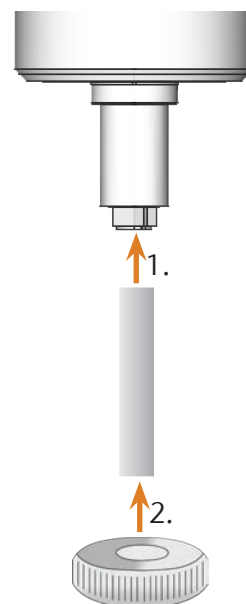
DÉMONTAGE DE LA PINCE DE SERRAGE
